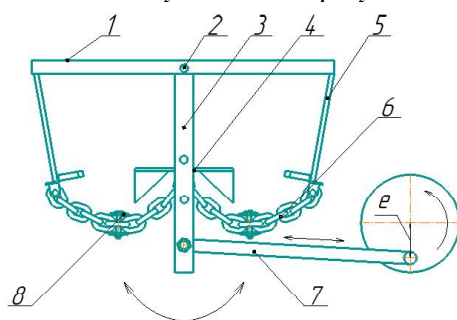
Схема рабочего оборудования цепного агрегата с волновой рабочей камерой
